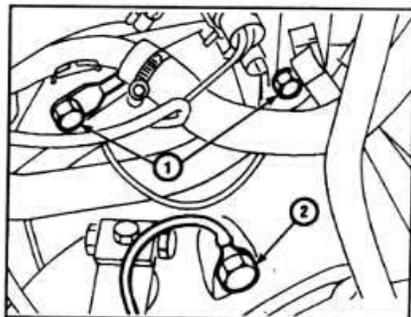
А.27. Расположение верхних болтов крепления коробки передач к двигателю (1) и болта крепления земляной шины (2).
